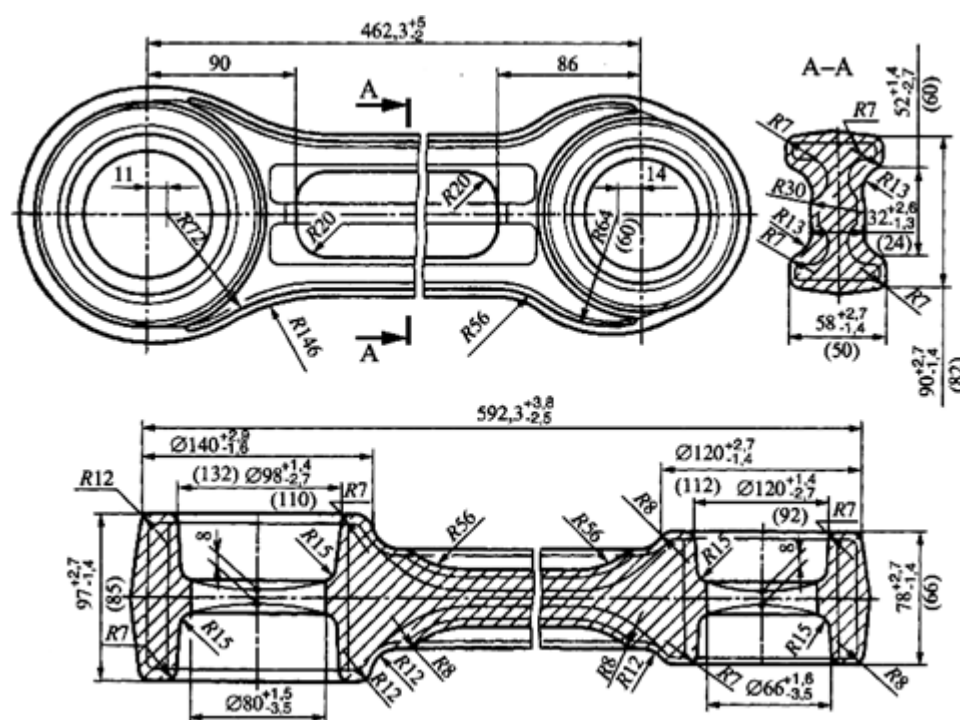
Чертёж типовой молотовой штамповки шатуна в открытом штампе.
